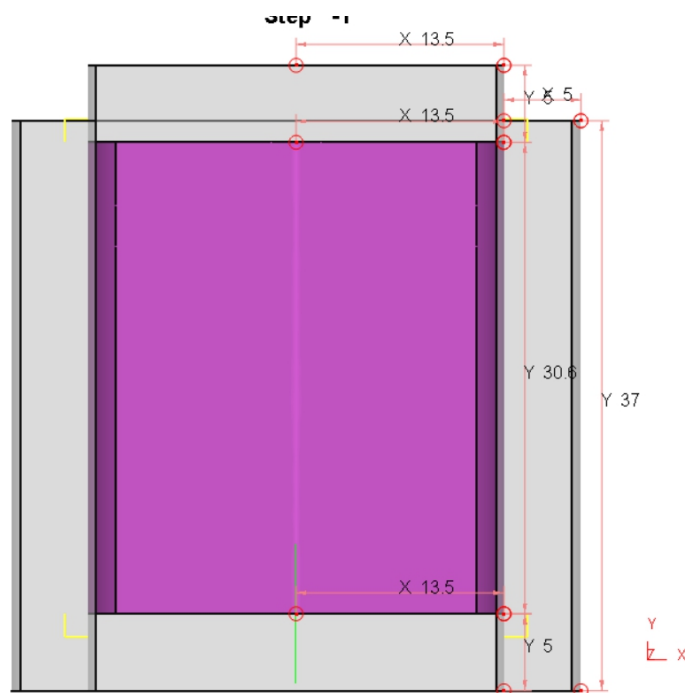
Модель збірки обичайка–пресовка з позначеними геометричними розмірами
